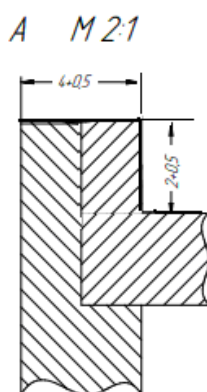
Размеры подготовки кромок корпуса и крышки под сварку
